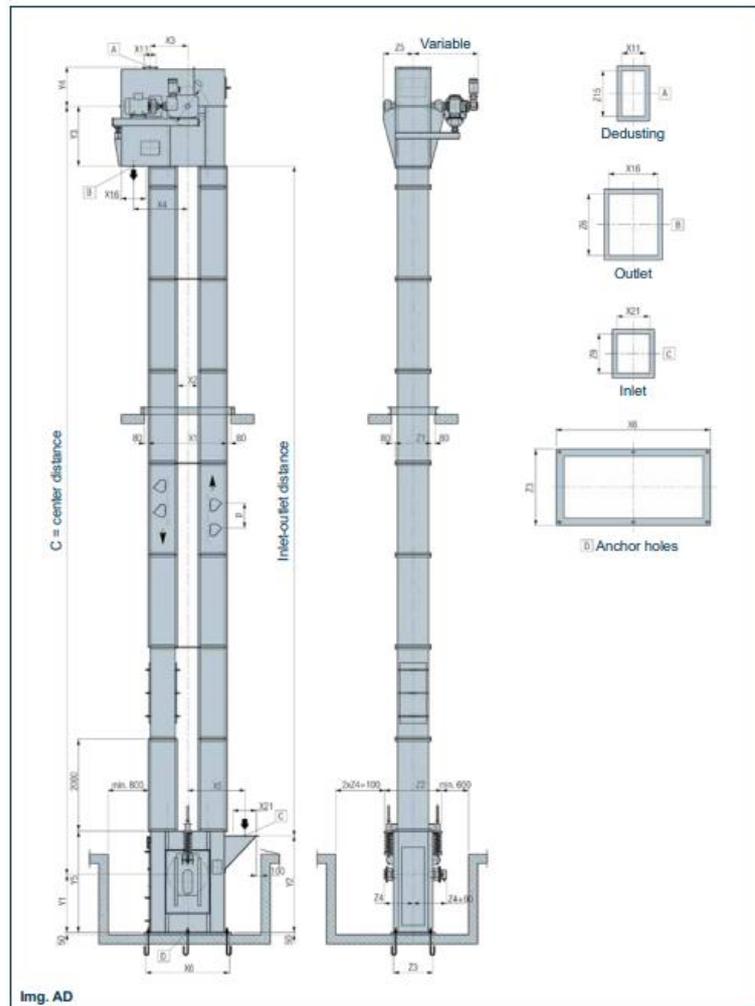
Croquis de dimensiones principales de elevador de cangilones. Fuente: GAMBAROTTA GSCHWENDT GmbH Advanced Conveyor Technology, https://www.rauscher-holstein.at/attachments/article/595/EN18_R1901_BUCKET%20ELEVATORS_low.pdf
